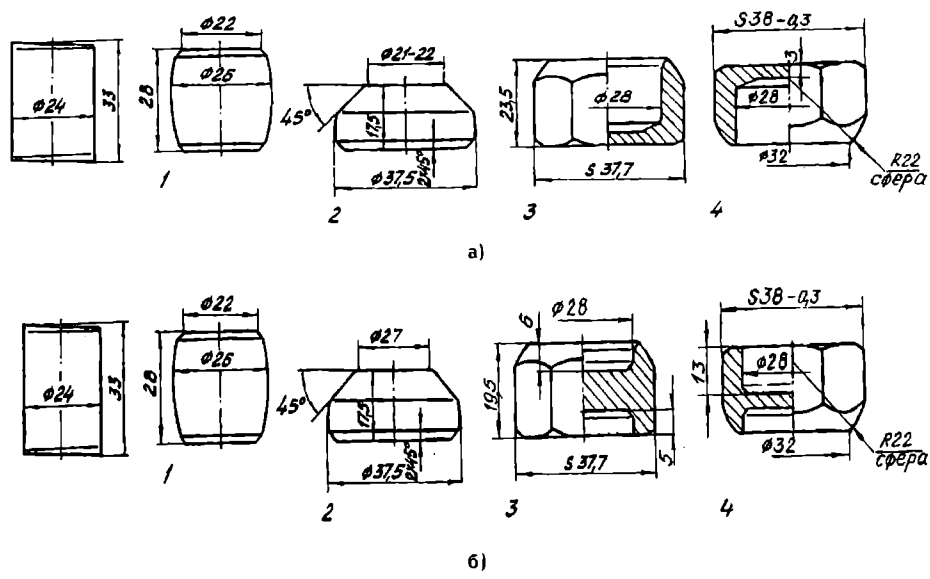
Переходы штамповки гайки колесной: 1 – осадка заготовки; 2 – высадка цилиндроконической заготовки; 3 – выдавливание с оформлением ребер; 4 – доштамповка с калибровкой сферы
